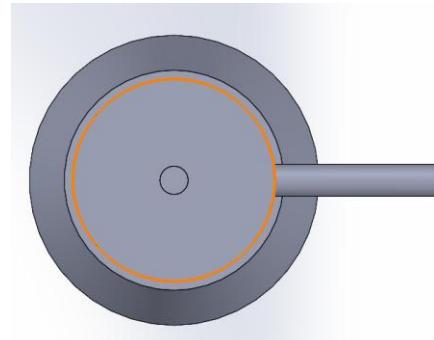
Vista superior del segundo diseño de flotador hidráulico.
